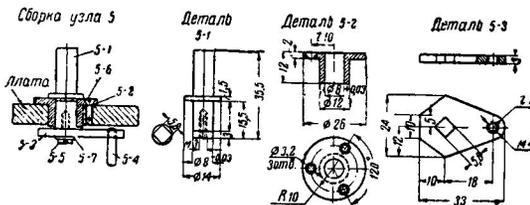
Переключатель (узел 5) и его детали: 5-1 — ось переключателя (сталь 45) — 1 шт.; 5-2 — втулка (сталь 3) — 1 шт.; 5-3 — фиксатор (сталь 20) — 1 шт.; 5-4 — палец (изготавливается из винта М4, сталь 45) — 1 шт.; 5-5 — винт М3 × 10 мм (сталь 3) — 1 шт.; 5-6 — винт М3 × 8 мм (сталь 3) — 3 шт.; 5-7 — шайба 3,2 мм (сталь 3) — 1 шт.
